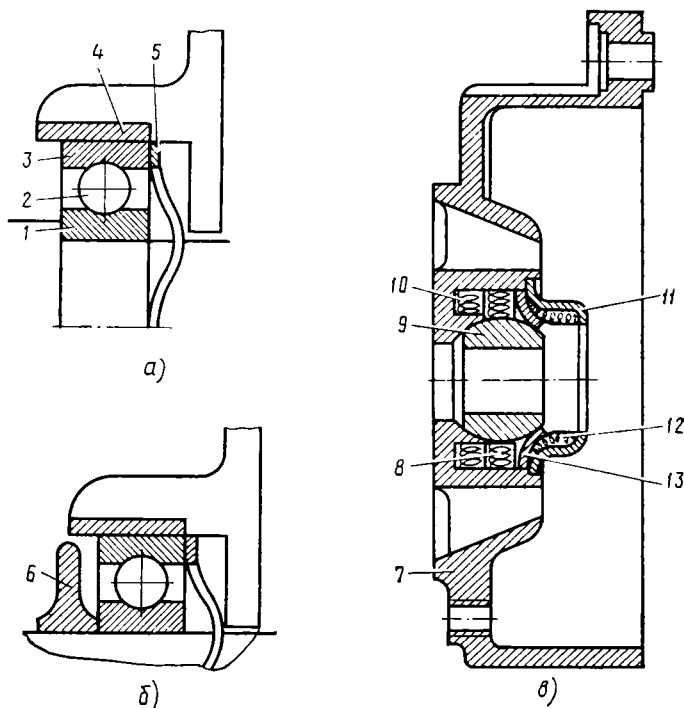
Установка подшипников качения (а — до упора в буртик вала, б — до упора в упорную шайбу) и подшипника скольжения в шит (в):
